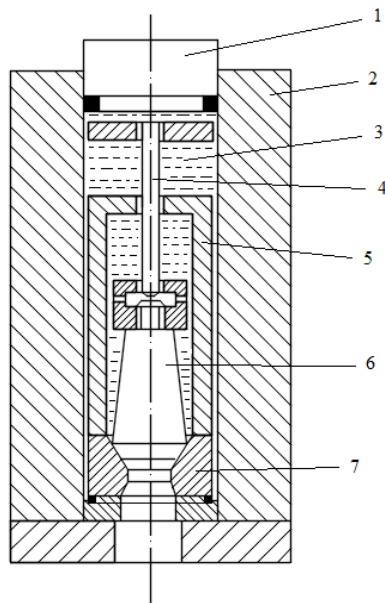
Наладка пластометра для испытания образцов на растяжение (а.с. 777543). 1 – пуансон; 2 – герметичный контейнер; 3 – рабочая среда; 4 – испытуемый образец; 5 – стакан; 6 – вспомогательный образец; 7 – матрица
